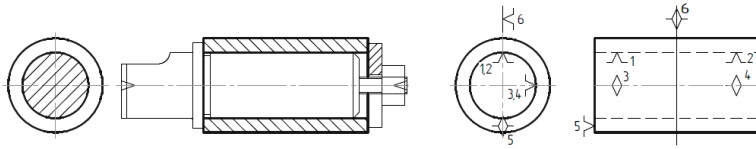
Схема базування втулки на циліндричній оправці з зазором.
